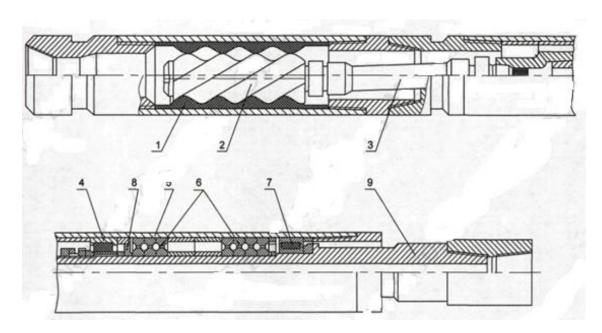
Типовая конструкция винтового забойного двигателя.
